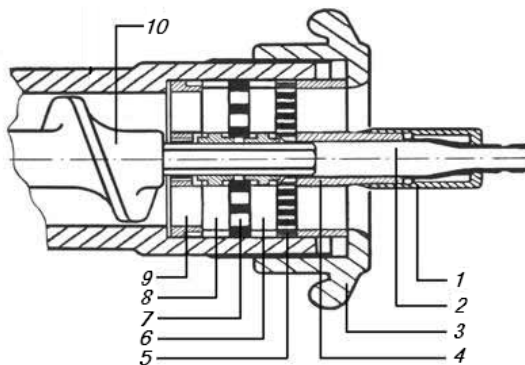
Ріжучий механізм вовчка з жилувальним комплектом: 1 – гільза; 2 – відвідна трубка; 3 – накидна гайка; 4 – опорне кільце; 5 – вихідна решітка; 6 – жилувальний ніж (тип «Турбо»); 7 – проміжна решітка; 8 – хрестоподібний двосторонній ніж; 9 – приймальна решітка з підшипником; 10 – робочий шнек.
